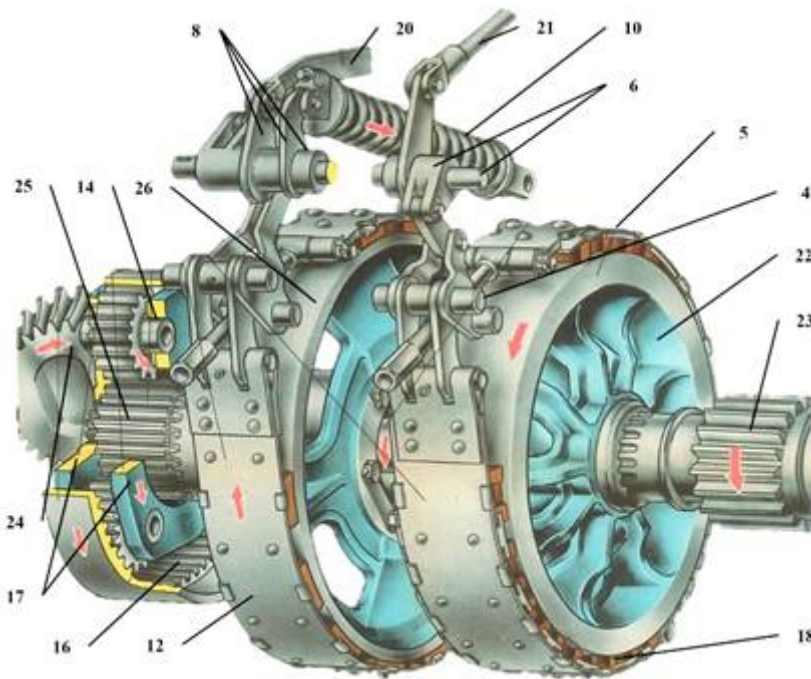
Планетарний механізм повороту трактора ДТ-75М:
